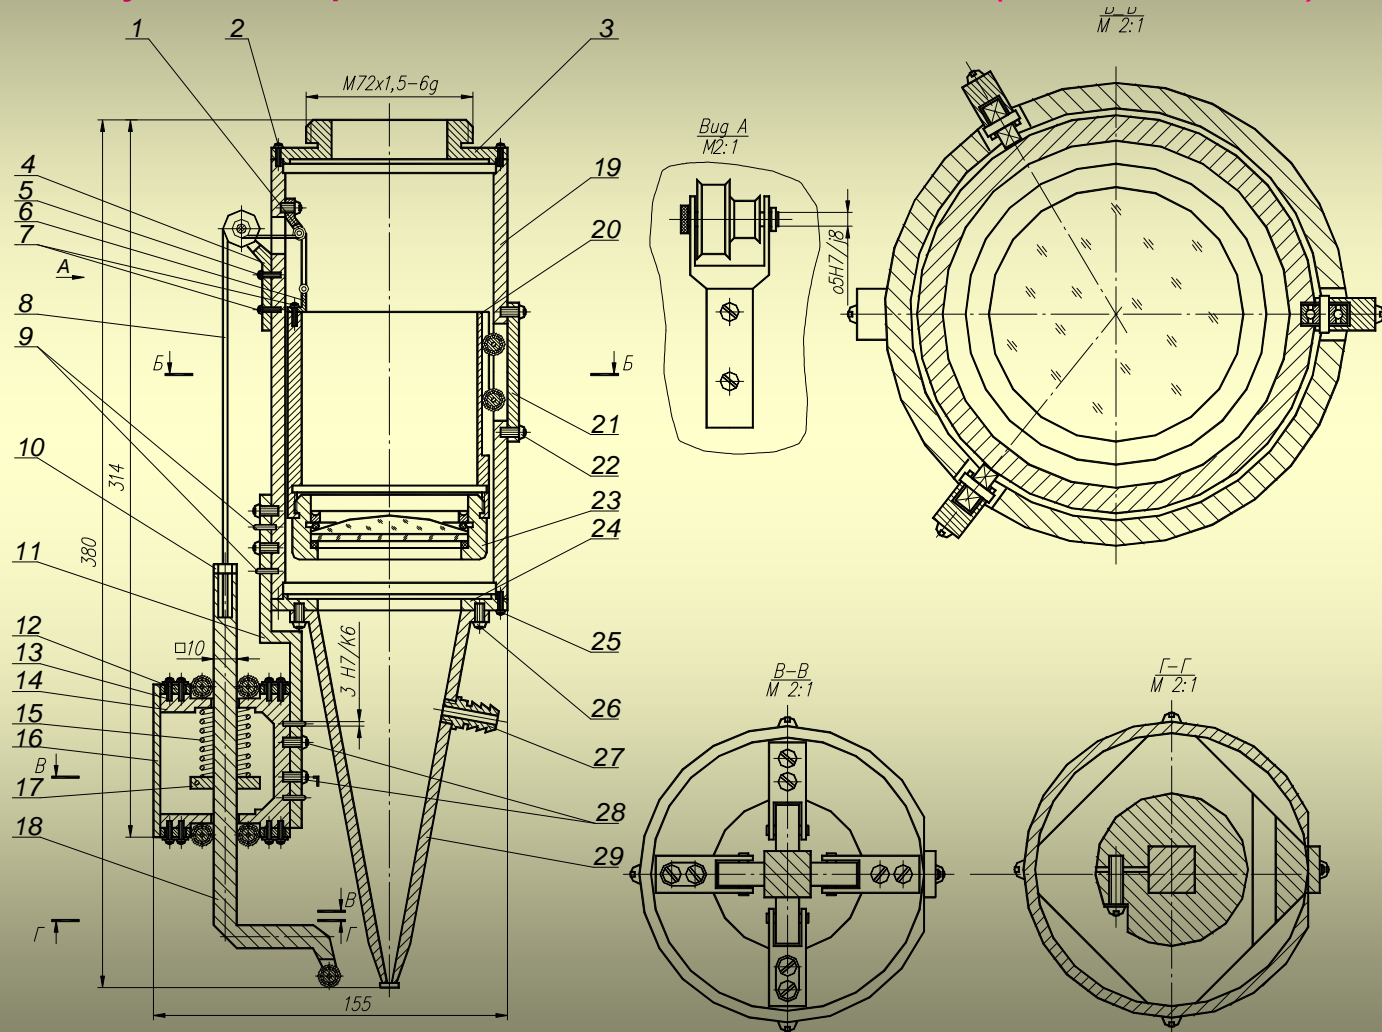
К. Фокусуюча система із змінним пристроєм для позиціювання відносно заготовки
